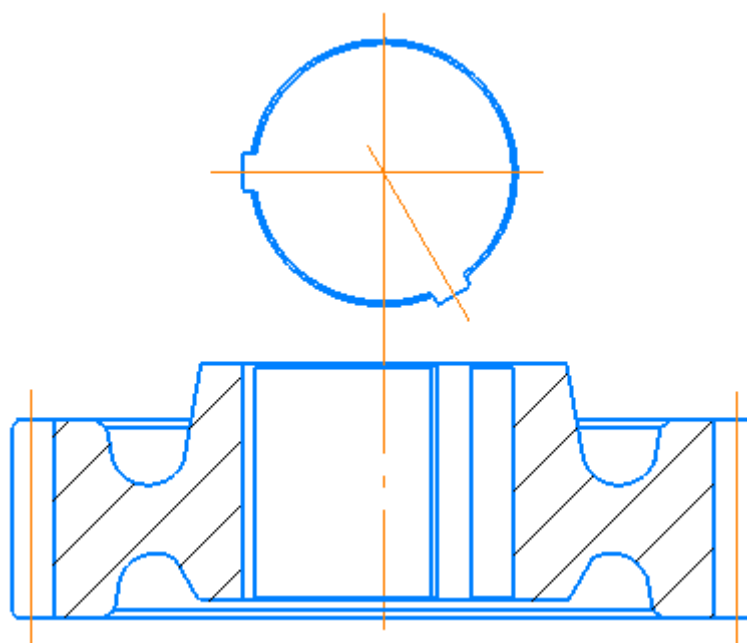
Эскиз детали «Колесо зубчатое»
